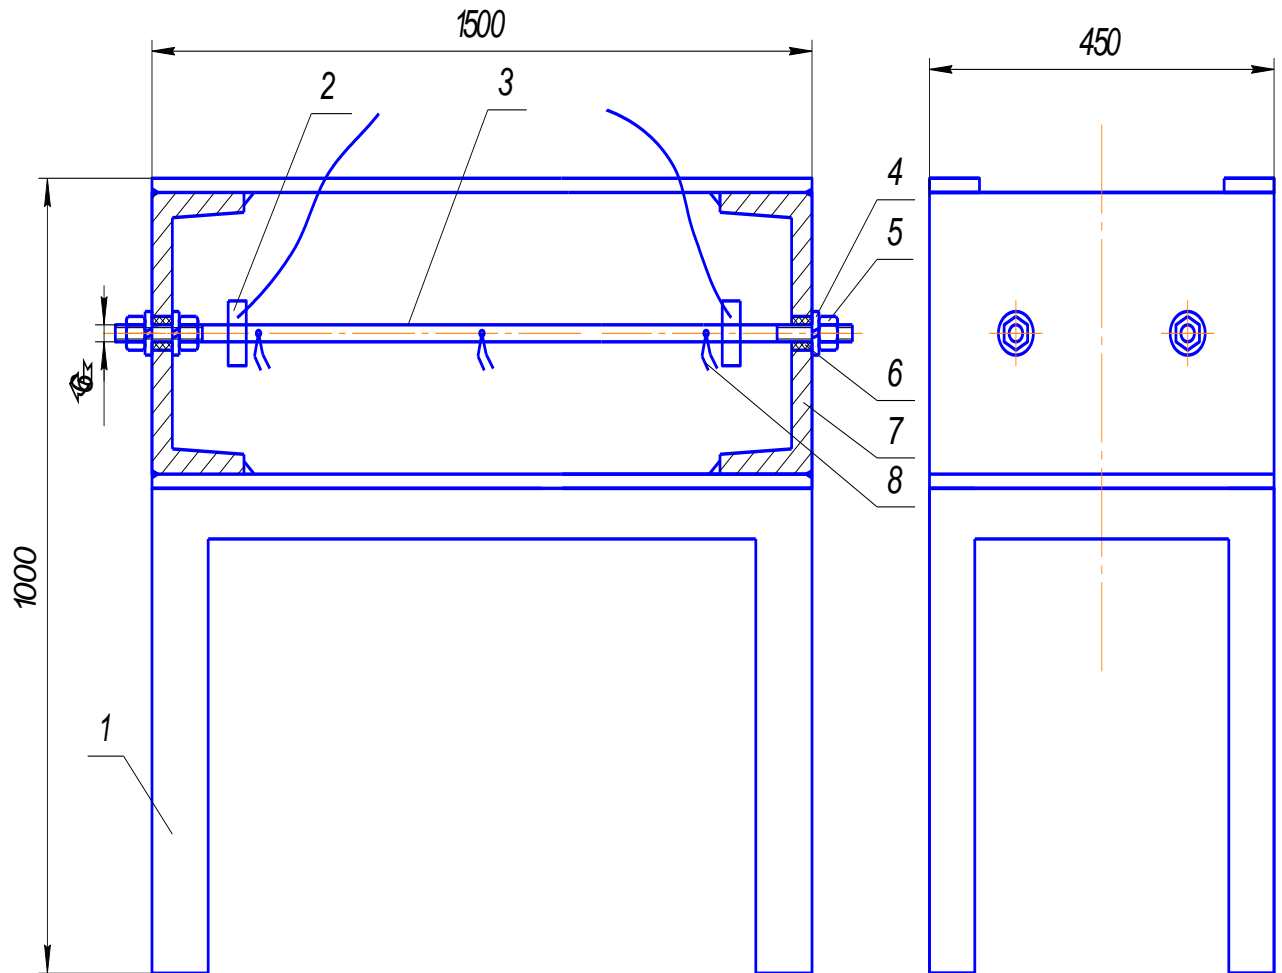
Схема лабораторної установки для термічного зміцнення пруткової арматури: 1 - корпус лабораторної установки зварної конструкції; 2 - мідні клєми контактні; 3 - арматурний пруток  $\varnothing 8$  мм; 4 - шайба; 5 – гайка М6; 6 - керамічні термостійкі втулки; 7 – швелер; 8 - термопари (хромель-алюмель).
